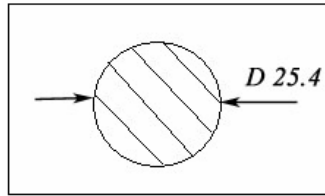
Sección transversal del Eje vertical en el extremo empotrado (medidas en milímetros)
